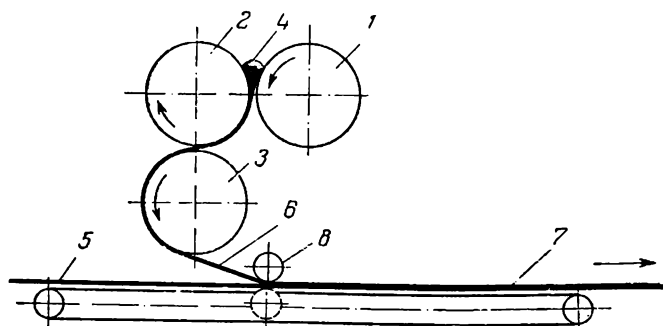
Схема выпуска резиновой прослойки на трехвалковом каландре и наложения ее на обрезиненный корд:
